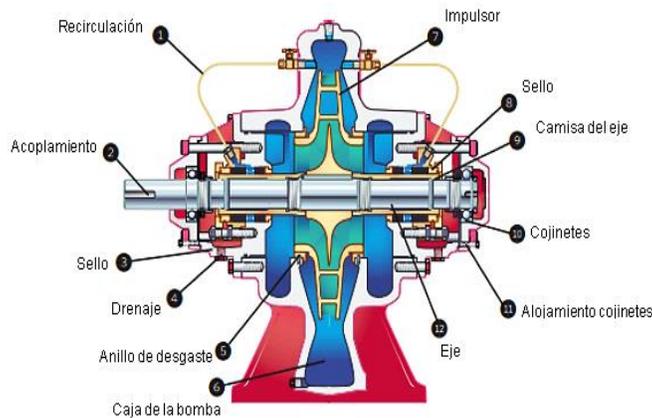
Principales partes de una bomba centrífuga mono-etapa radial
